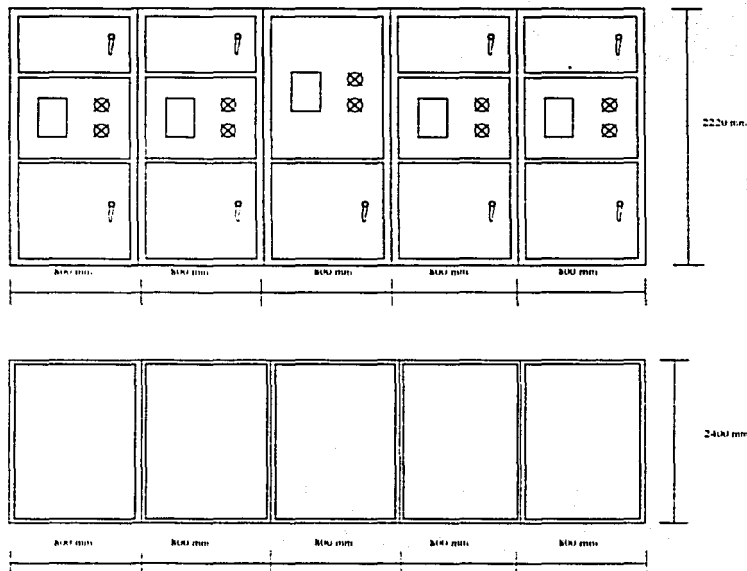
Vista frontal y de planta de un tablero metal-clad en 13.8 kV
